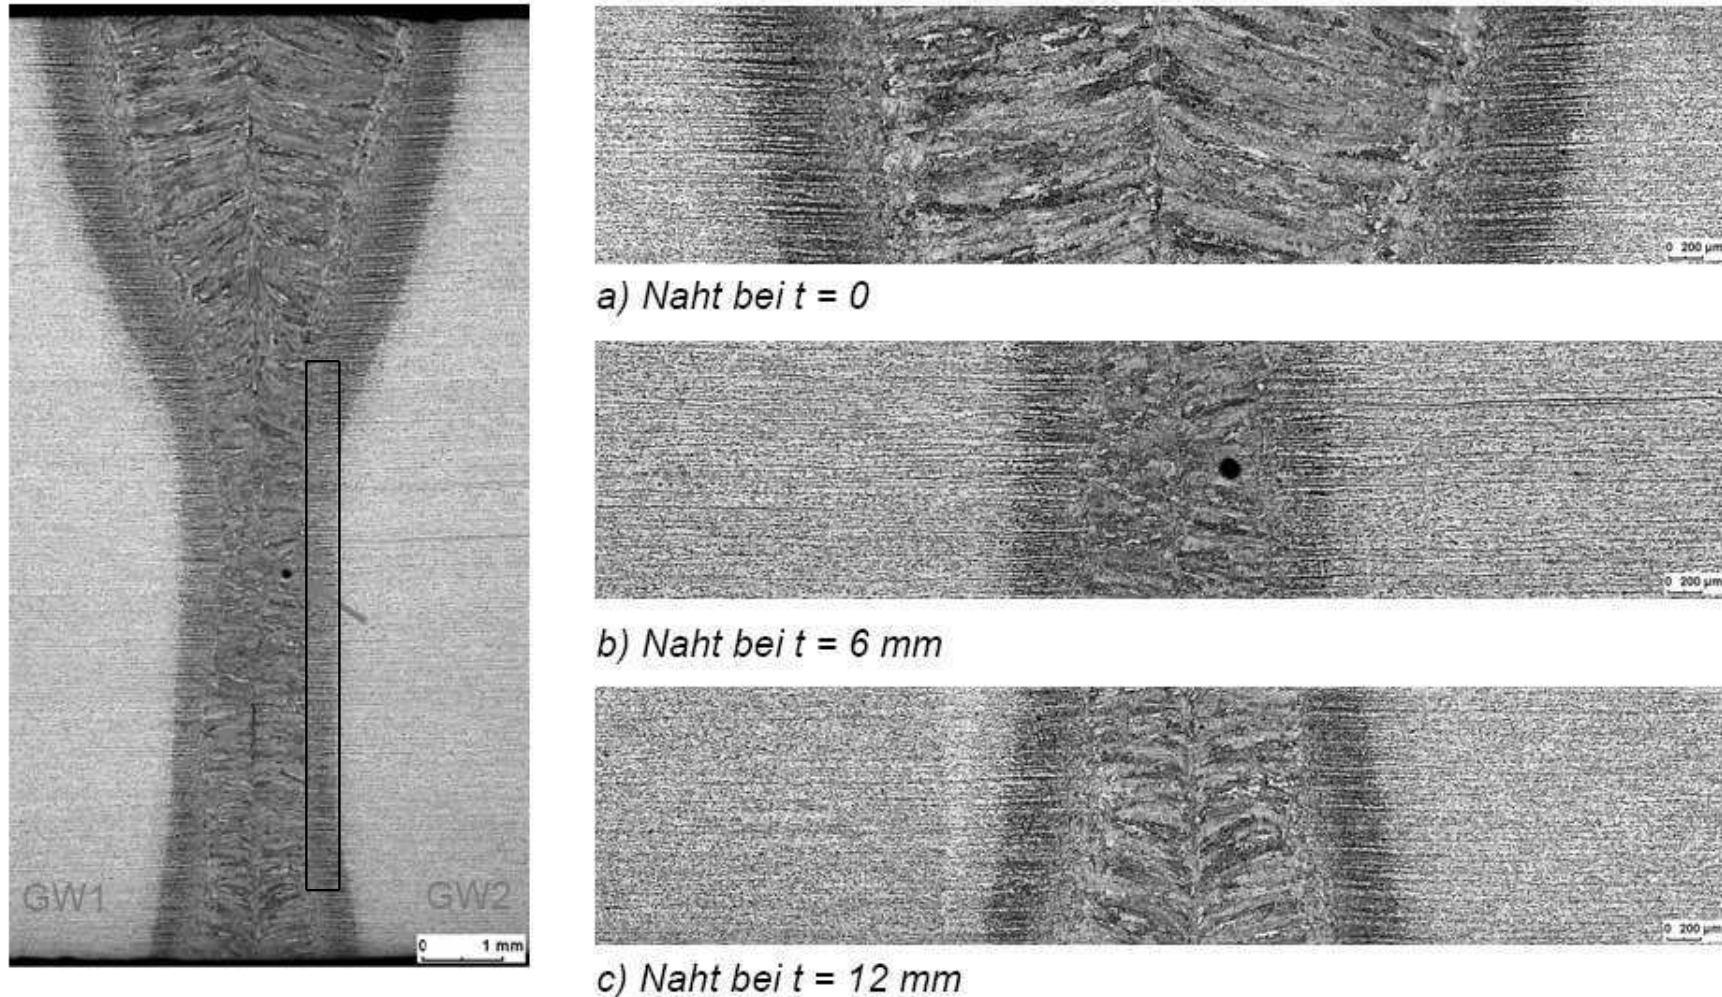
Makroaufnahme der Schweißnaht
